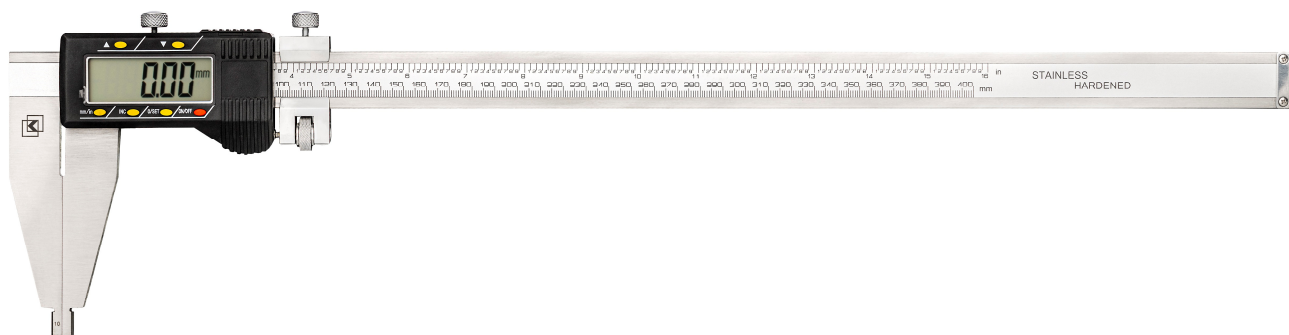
Общий вид штангенциркулей ШЦЦ-III
